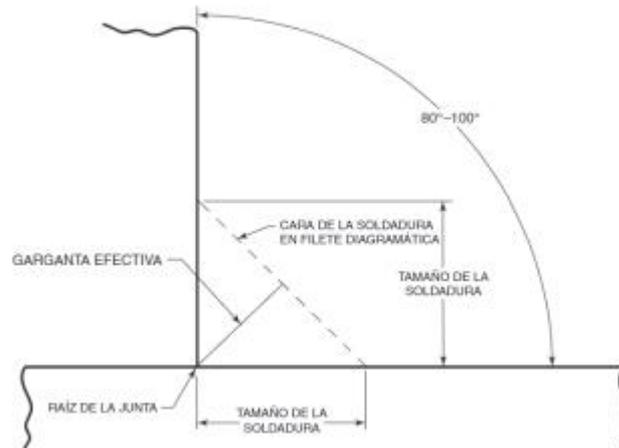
Soldadura en filete (ver 4.4.2.6)
